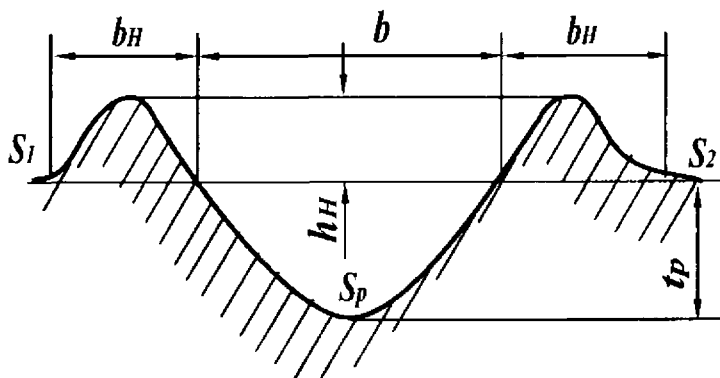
Поперечный профиль шлифовальной риски с наплывами
